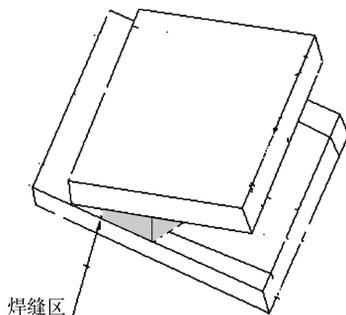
板材斜 T 形接头的焊缝示意图
